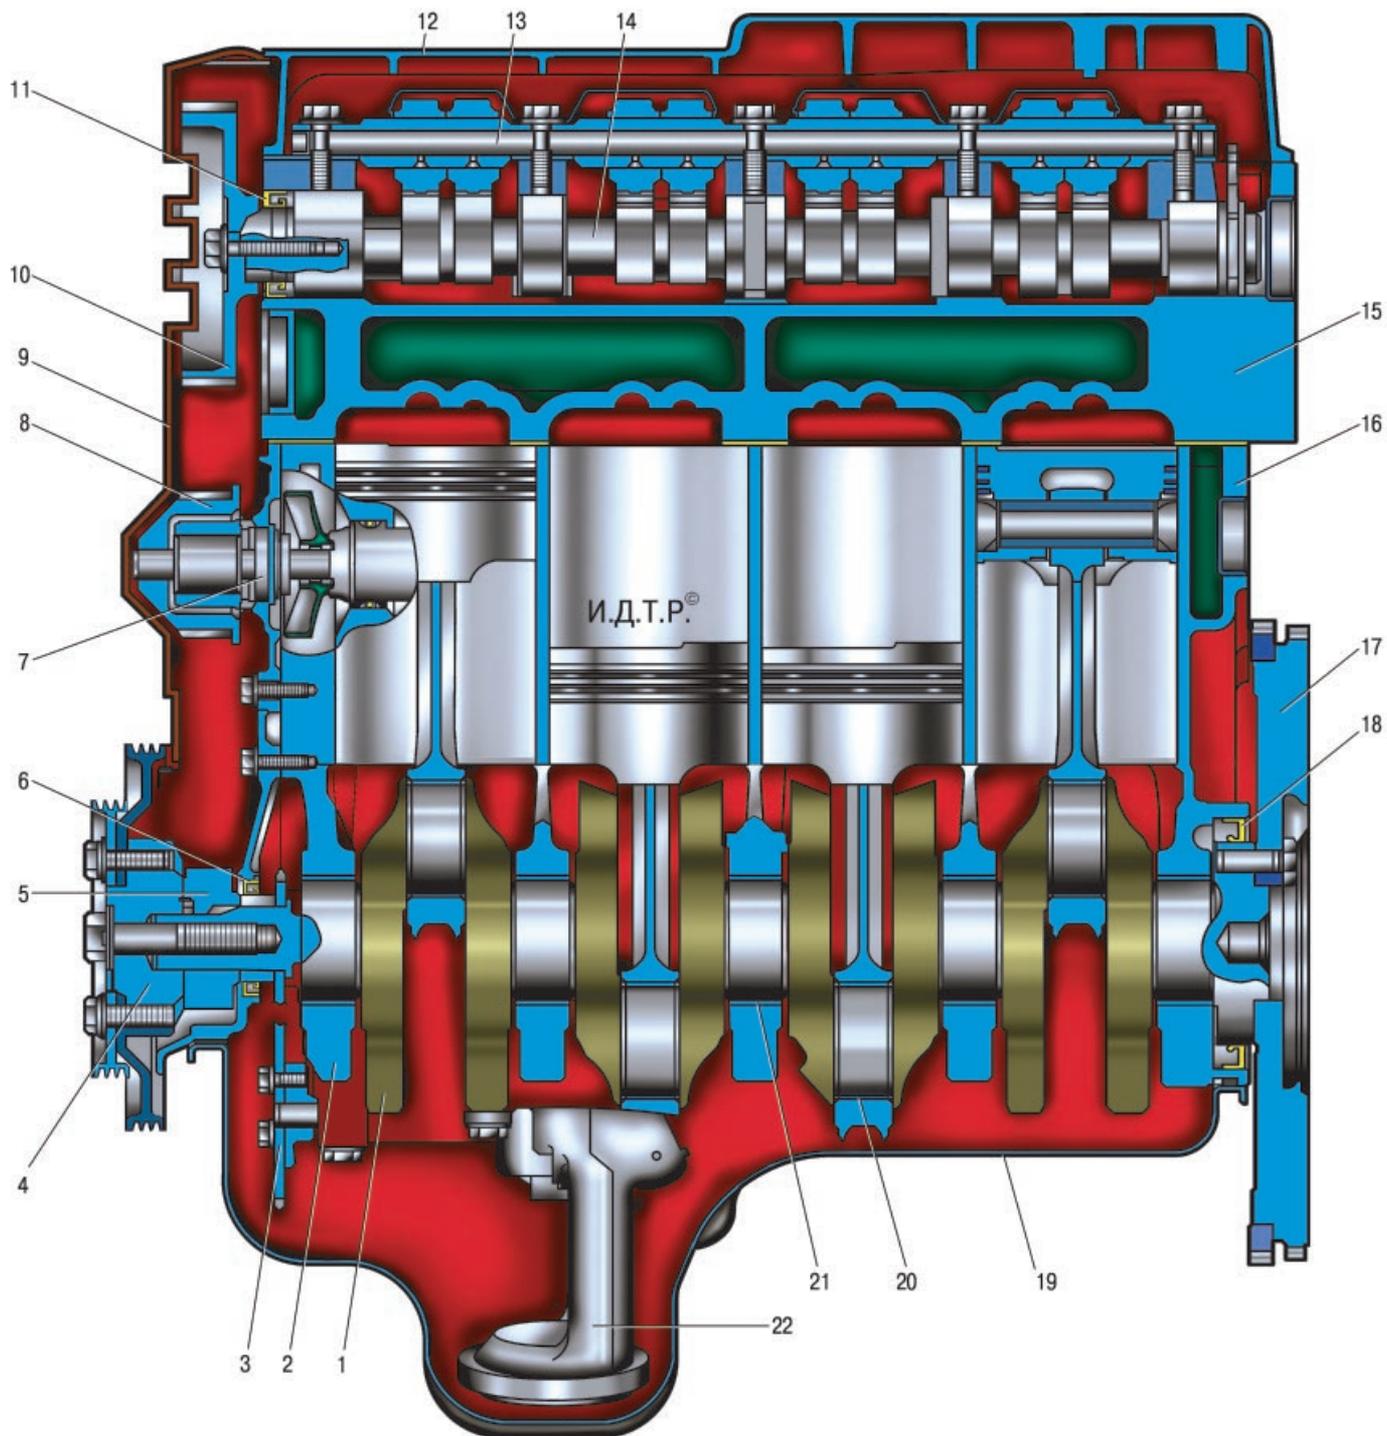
Двигатель K7J (продольный разрез): 1 – коленчатый вал; 2 – крышка коренного подшипника коленчатого вала; 3 – звездочка цепи привода масляного насоса; 4 – шкив ремня привода вспомогательных агрегатов; 5 – зубчатый шкив коленчатого вала; 6 – передний сальник коленчатого вала; 7 – водяной насос; 8 – зубчатый шкив водяного насоса; 9 – крышка ремня привода газораспределительного механизма; 10 – зубчатый шкив распределительного вала; 11 – сальник распределительного вала; 12 – крышка головки блока цилиндров; 13 – ось коромысел привода клапанов; 14 – распределительный вал; 15 – головка блоков цилиндров; 16 – блок цилиндров; 17 – маховик; 18 – задний сальник коленчатого вала; 19 – масляный картер; 20 – вкладыш шатунного подшипника; 21 – вкладыш коренного подшипника; 22 – приемный патрубок масляного насоса
